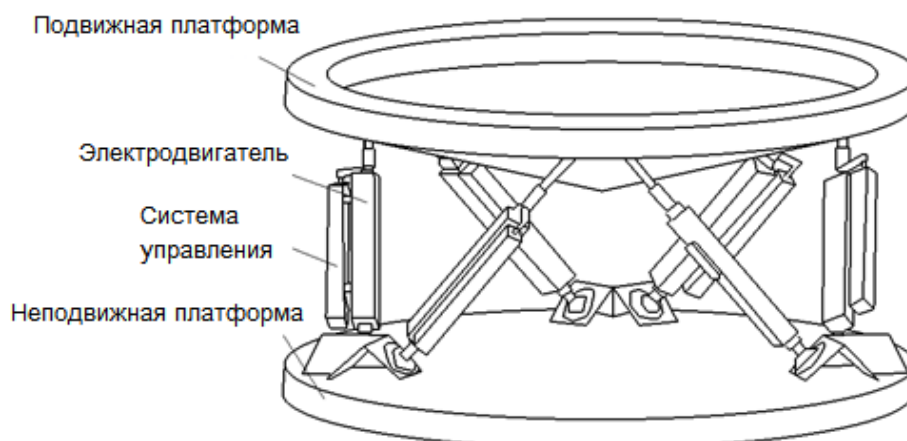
Конструкция периферийного стыковочного механизма с управляемыми штангами
